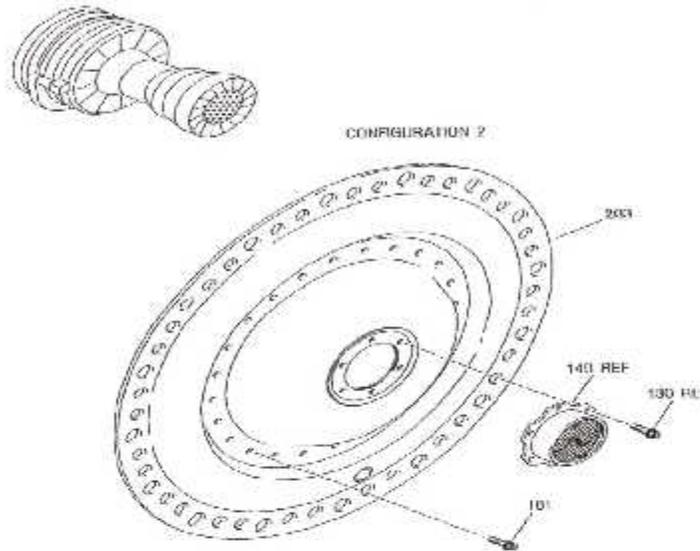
Enlèvement des Brides d'Assemblage.
